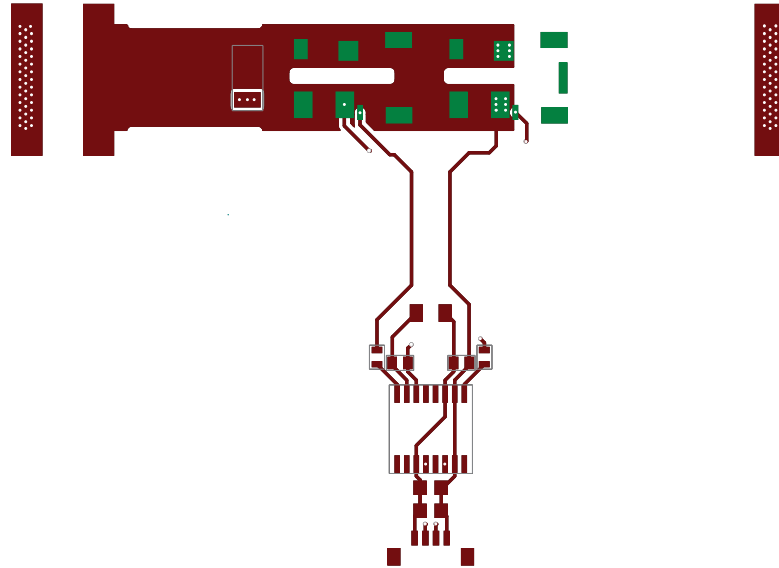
Trilhagem do PCB Flexível – Camada F.Cuivre.
